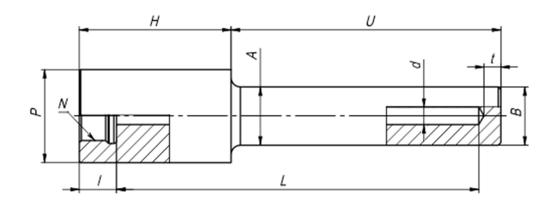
Гильза под приварку через адаптер (Socket Weld), цельноточёная, прямая, под подвижный штуцер.
